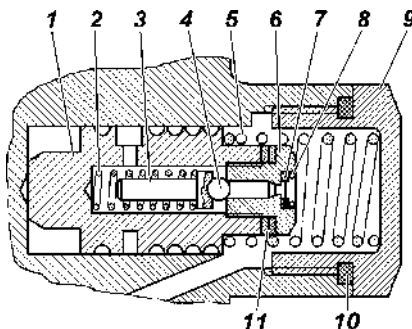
Auslass- und Vorsteuerventil der Pumpe: 1 – Schieber des Auslassventils; 2 – Feder des Rückschlagventils; 3 – Federhalterung des Rückschlagventils; 4 – Dichtung des Rückschlagventils; 5 – Ventillfeder; 6 – Sitz des Rückschlagventils; 7 – Filter; 8 – Ring; 9 – Blindstopfen; 10 – Dichtungsring; 11 – Einstellringe
